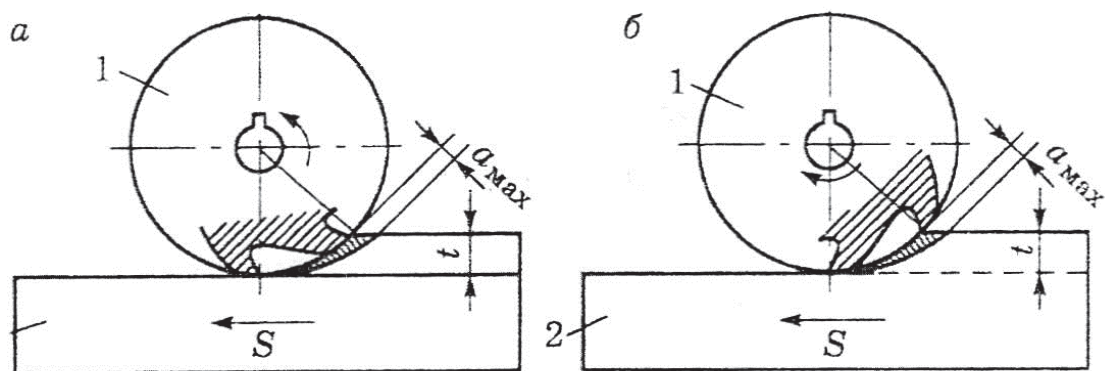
Схемы фрезерования: *а* – встречное; *б* – попутное; 1 – фреза; 2 – заготовка
